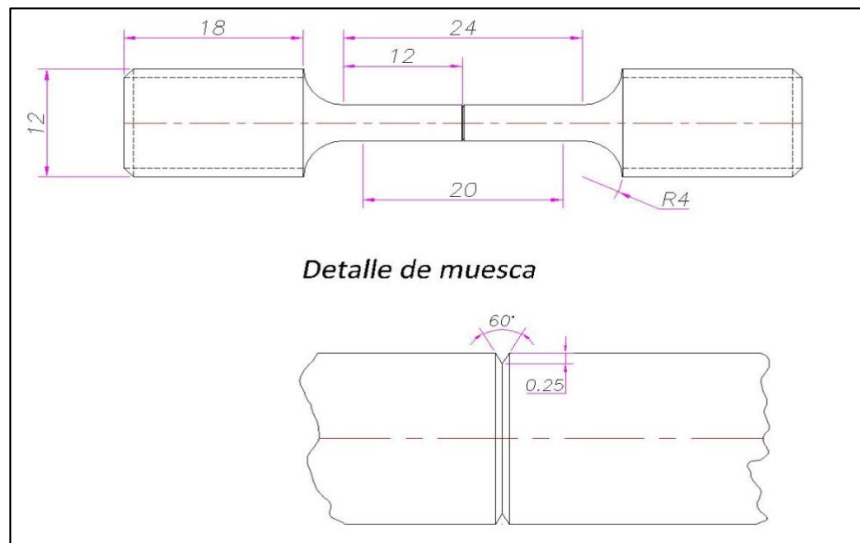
Dimensiones de la Probeta Calibrada con muesca
